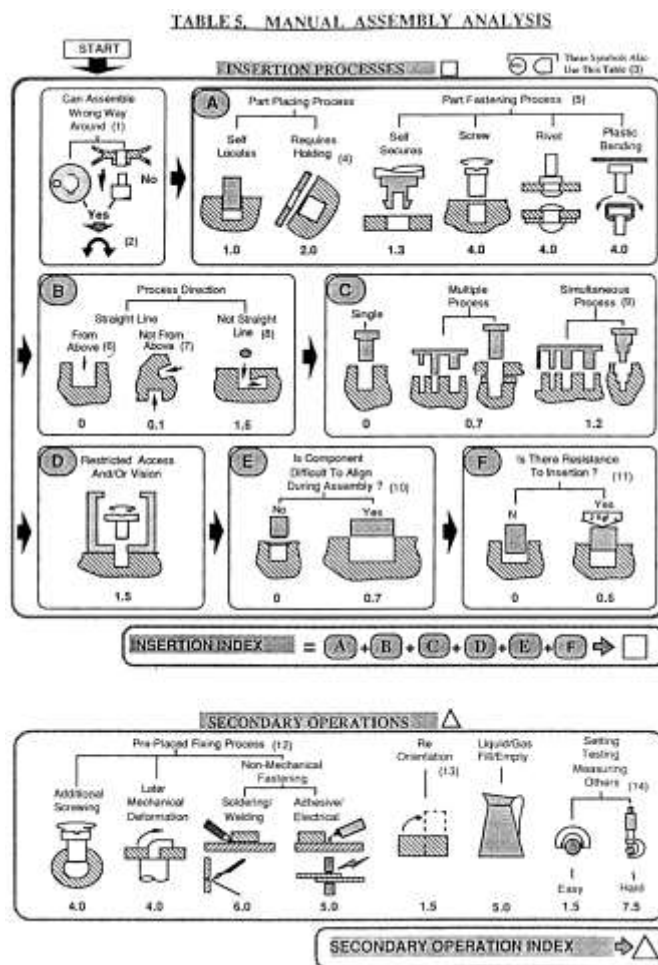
«Design for assembly/manufacturing analysis practitioners manual»
